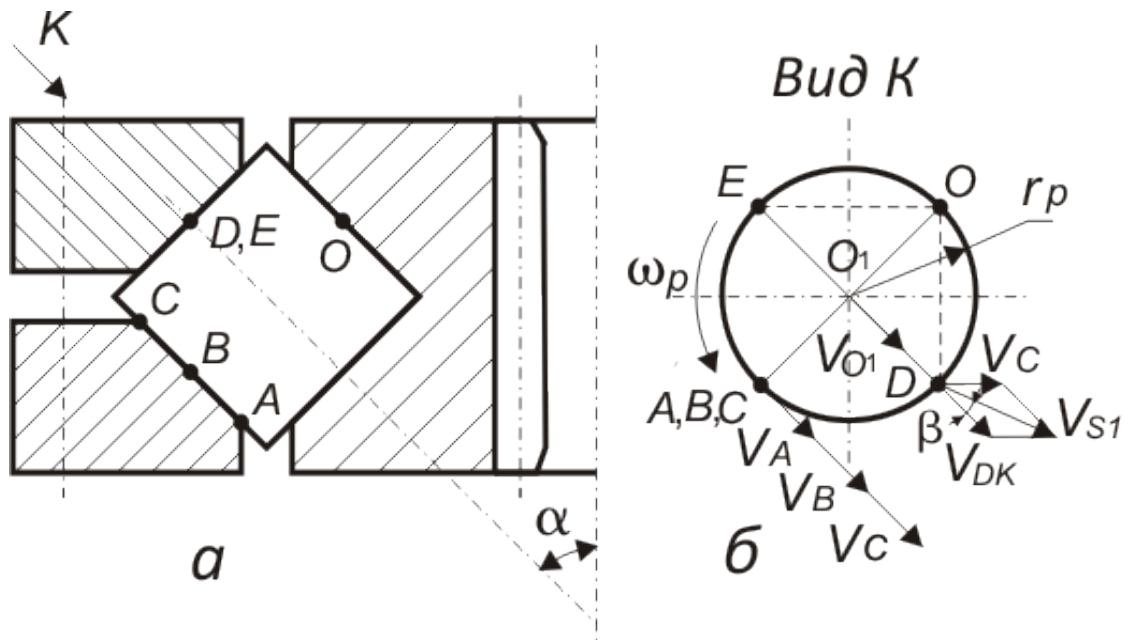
Частина конструкції опорно-поворотного пристрою: *a* – загальний вигляд; *б* – вид *K* на зовнішній торець ролика
